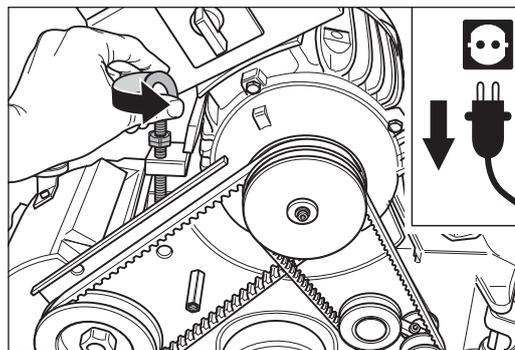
Die Ringschraube am Motor gegen den Uhrzeigersinn drehen.
